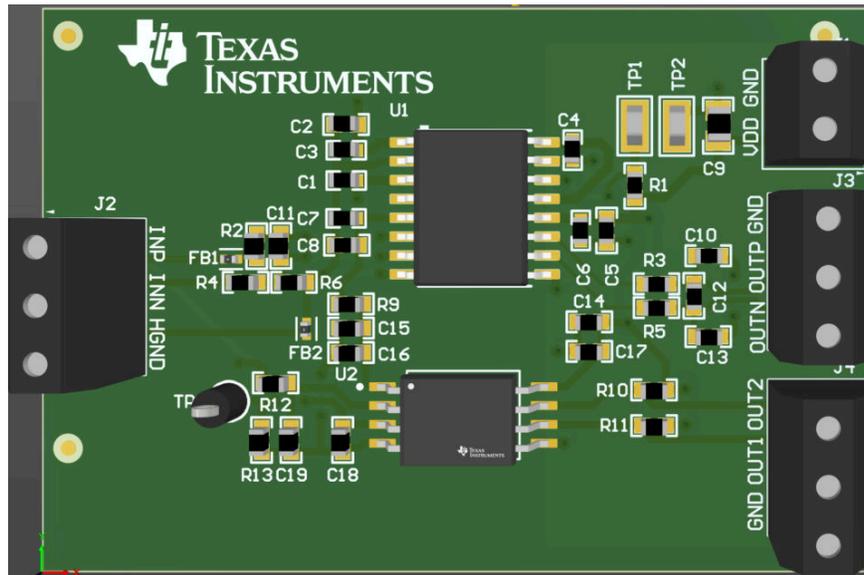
AMC3311 및 AMC23C11 PCB 레이아웃
